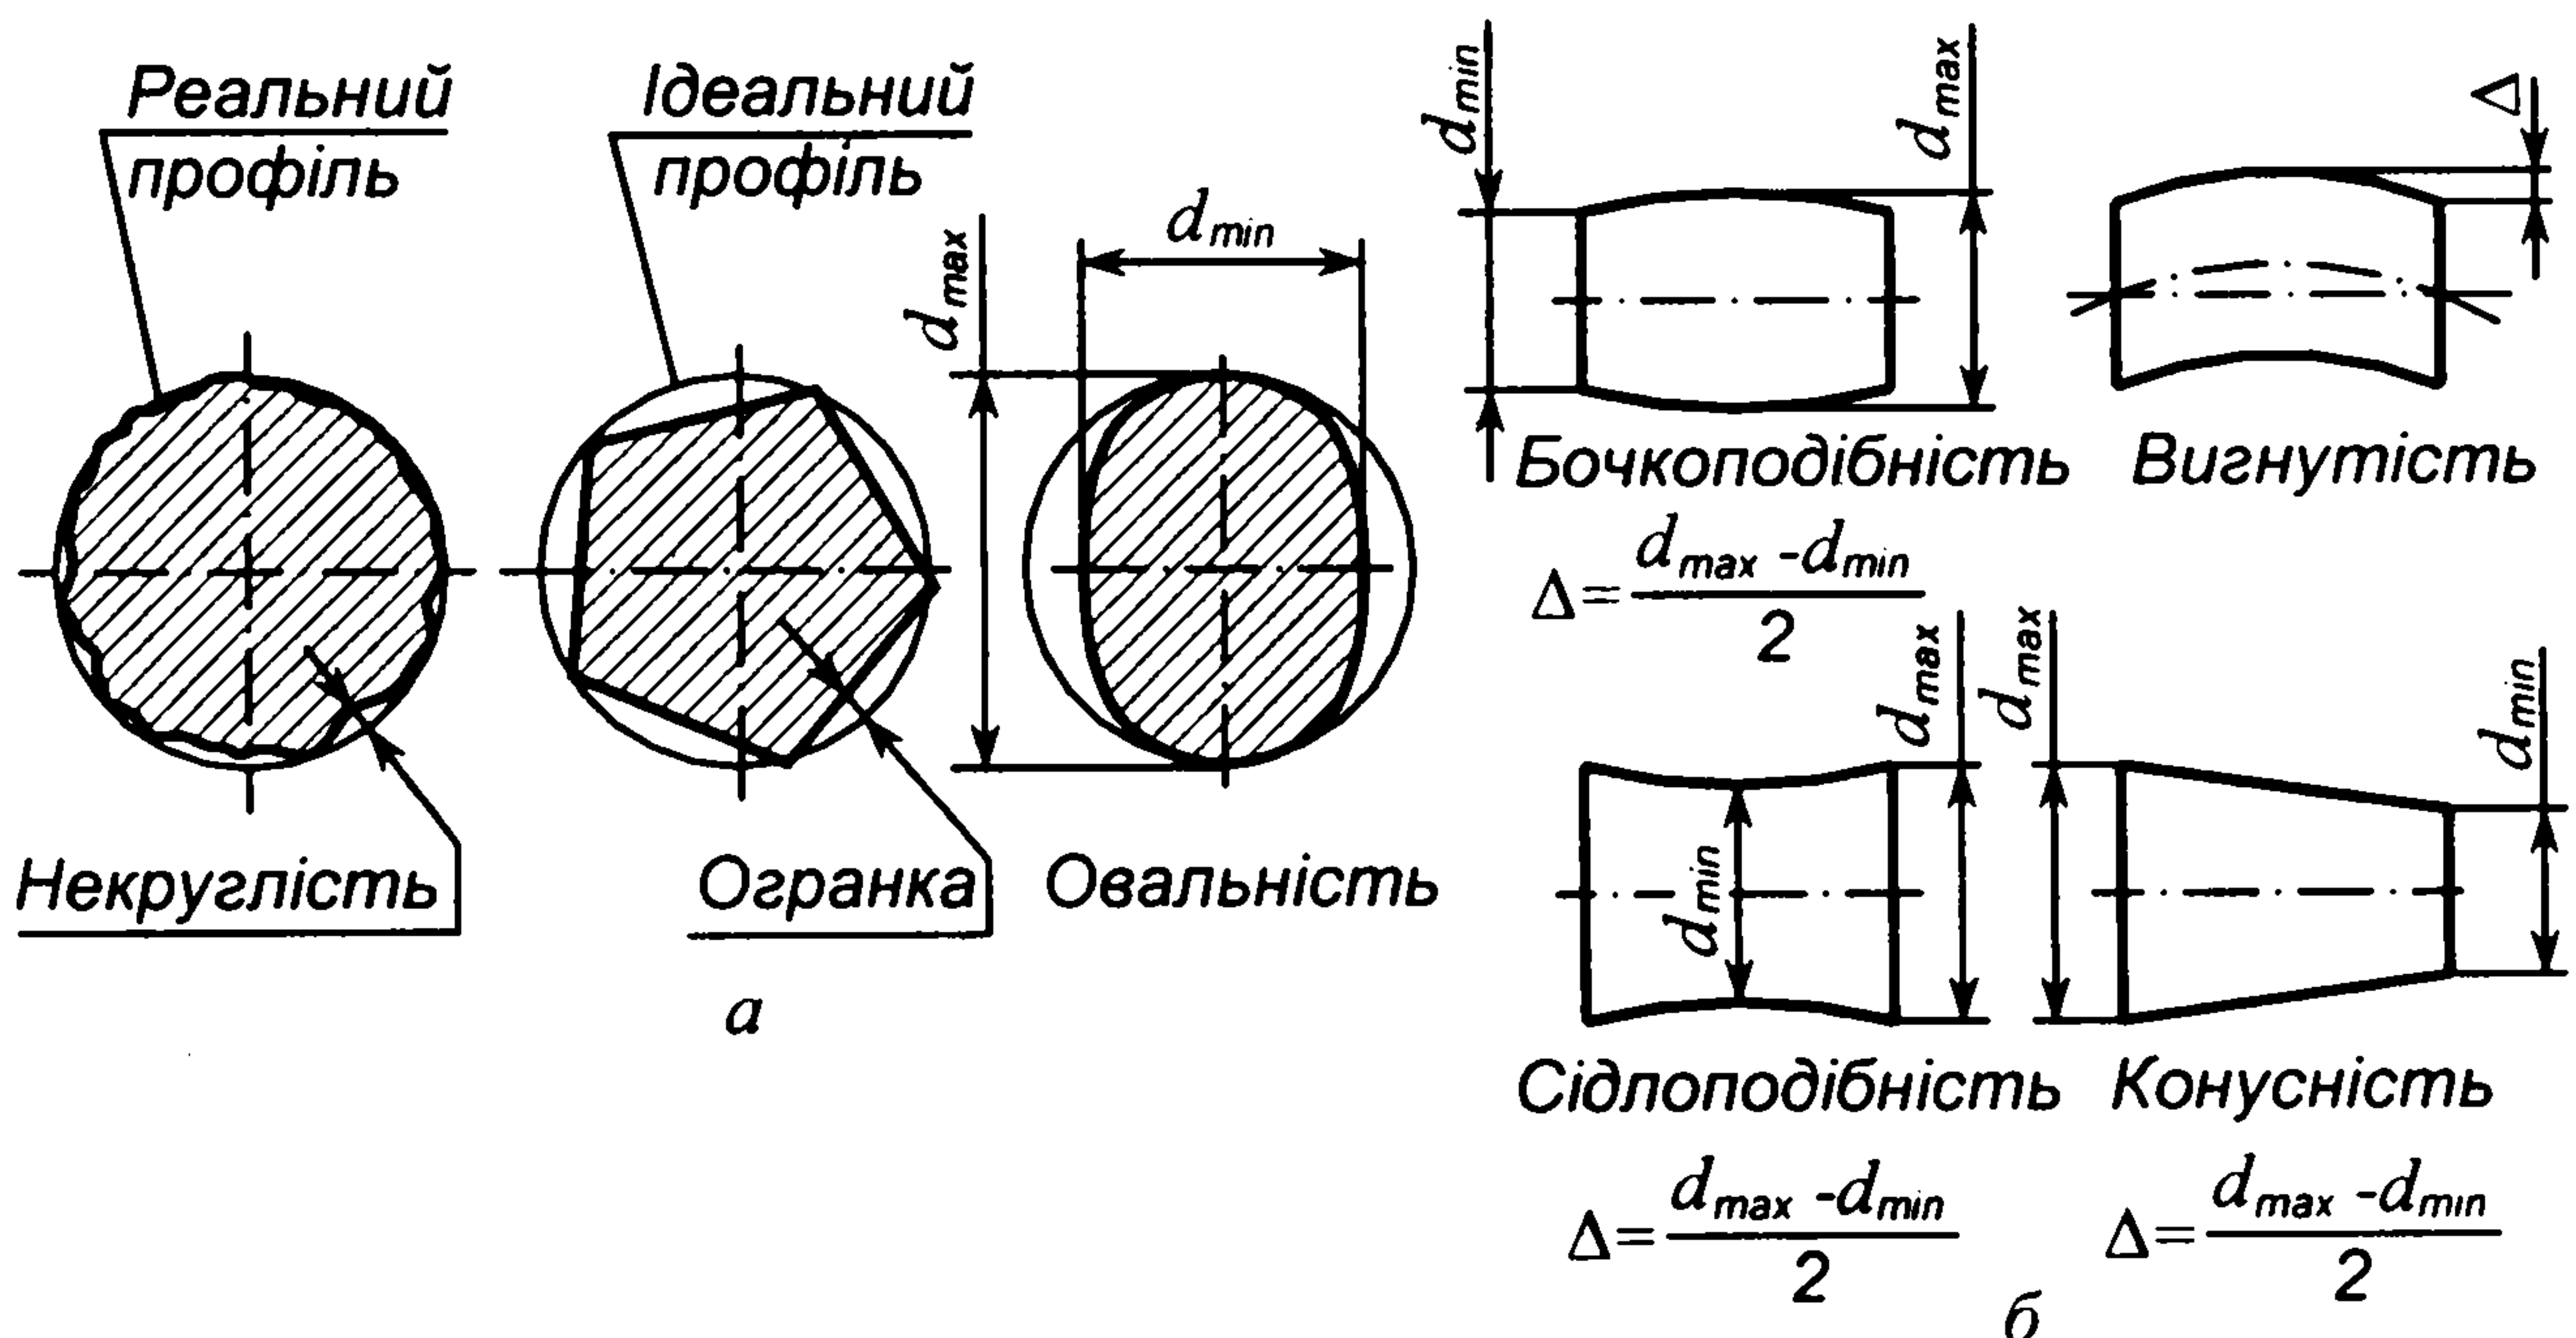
Відхилення форми деталей із циліндричними поверхнями
